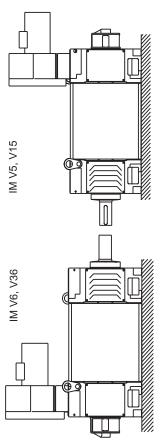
Disposición de las chapas de rejillas tipo branquias en las diversas formas constructivas
